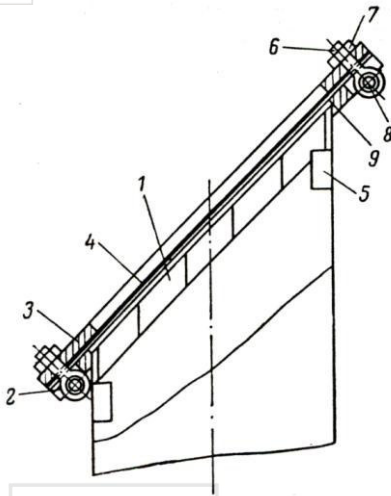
Похилий запобіжний клапан: 1-решітка; 2-фланець нижній; 3-фланець верхній; 4-діафрагма; 5-упор; 6-болт відкідний; 7-гайка; 8-вісь; 9-прокладка
